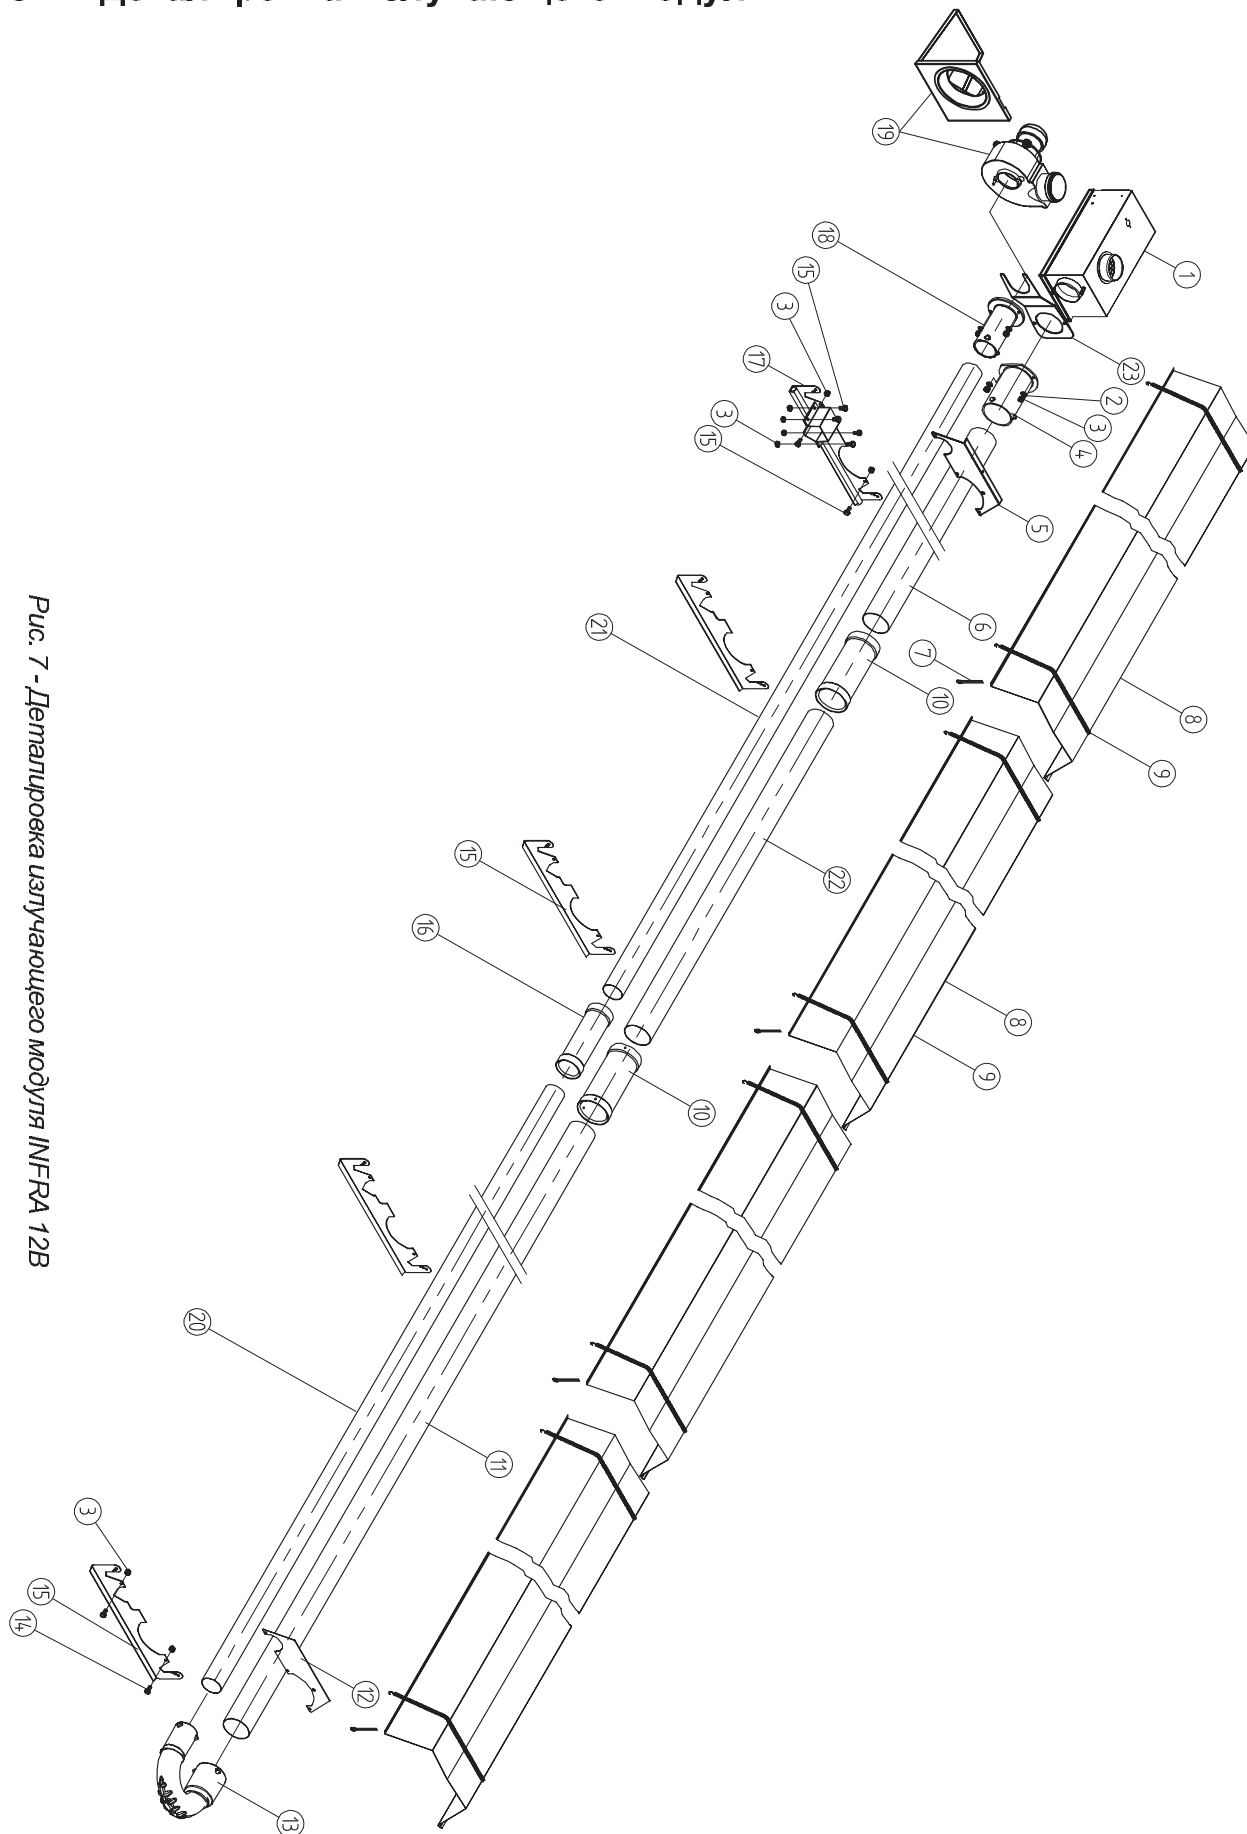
Детализовка излучающего модуля INFRA 12B
